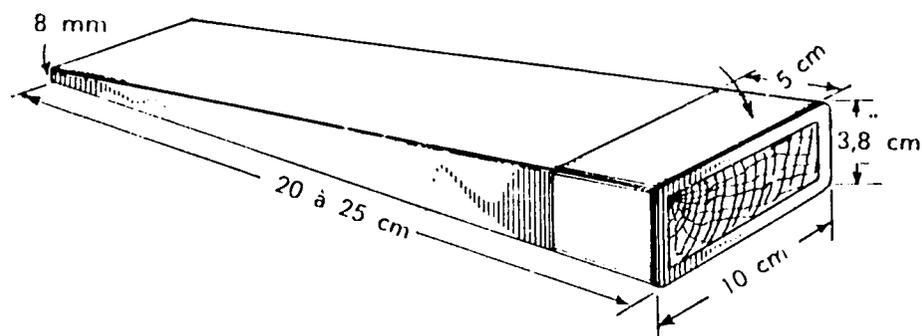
Coin de bois pour travail à la scie à chaîne. On utilise aussi avec ces scies des coins en aluminium et magnésium.
